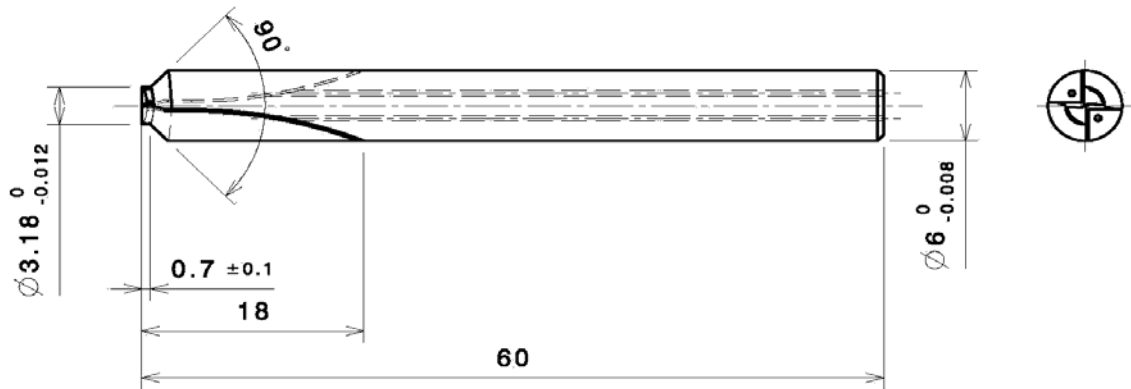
Креслення твердосплавного свердла BOF D3.18X0.7X 60-6 зі сплаву UF10
